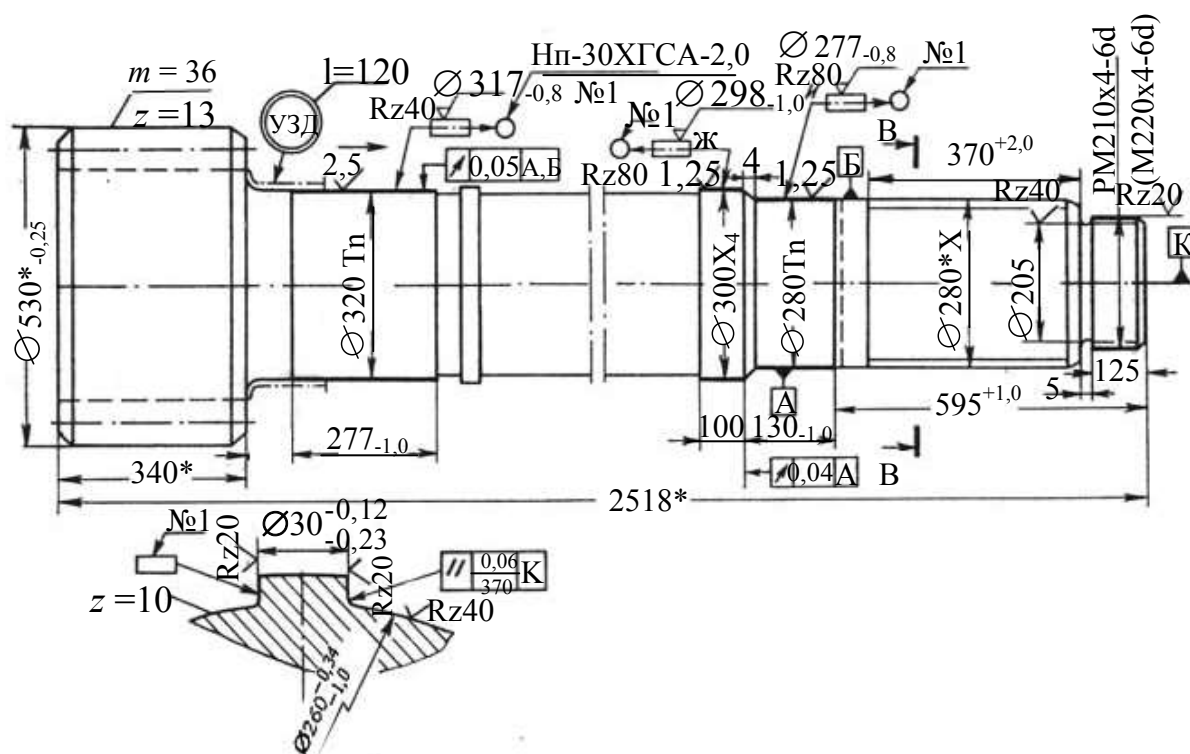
Ремонтный чертеж вал-шестерни ($m = 36$, $z = 13$) редуктора поворотного механизма: * – размеры справочные по чертежу
